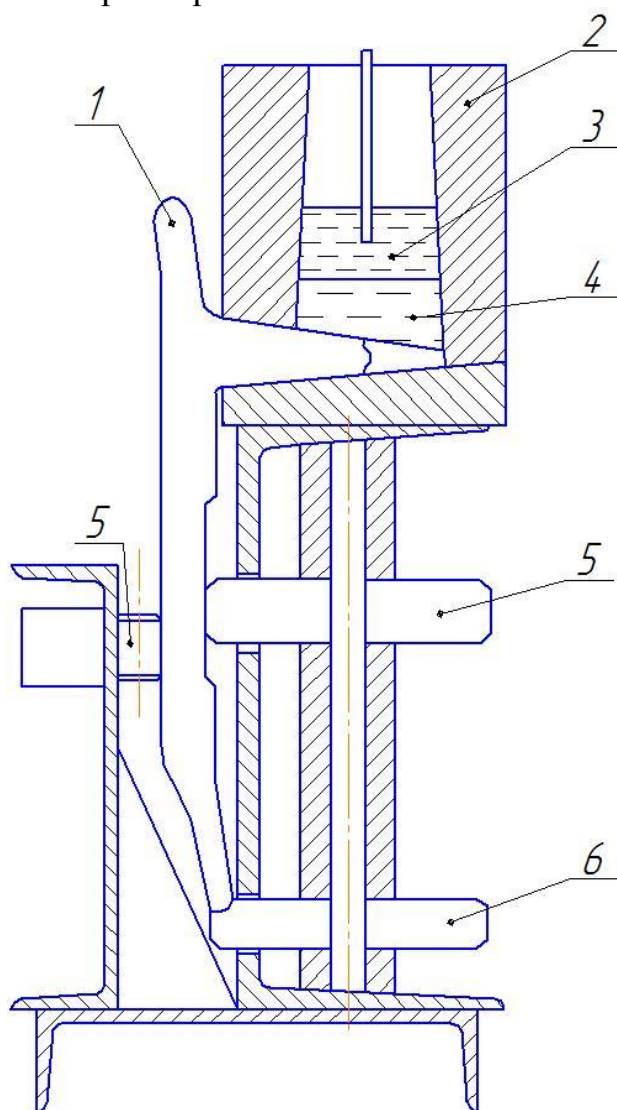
Схема электрошлаковой наплавки: 1 – трак; 2 – кристаллизатор; 3 – шлаковая ванна; 4 – металлическая ванна; 5 – ролики опорные; 6 – ролик опорный
